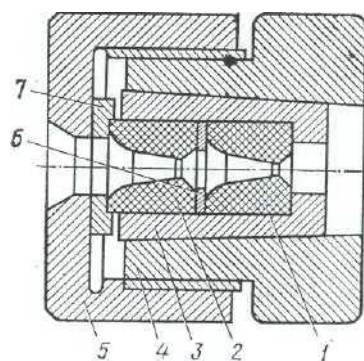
Збірна волюка для волочіння дроту в режимі гідродинамічного тертя: 1 – робочий твердосплавний вкладиш; 2 – напірний вкладиш; 3 – затискна втулка; 4 – корпус; 5 – гайка; 6 – ущільнення; 7 – завзята шайба
